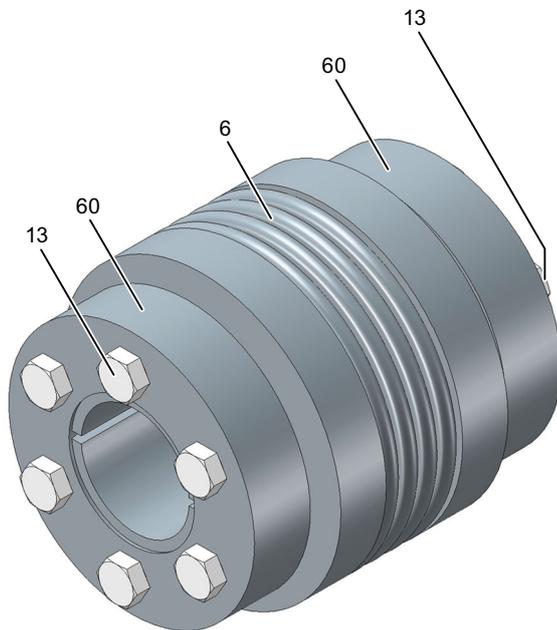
Ersatzteilzeichnung für Bauart SKK
